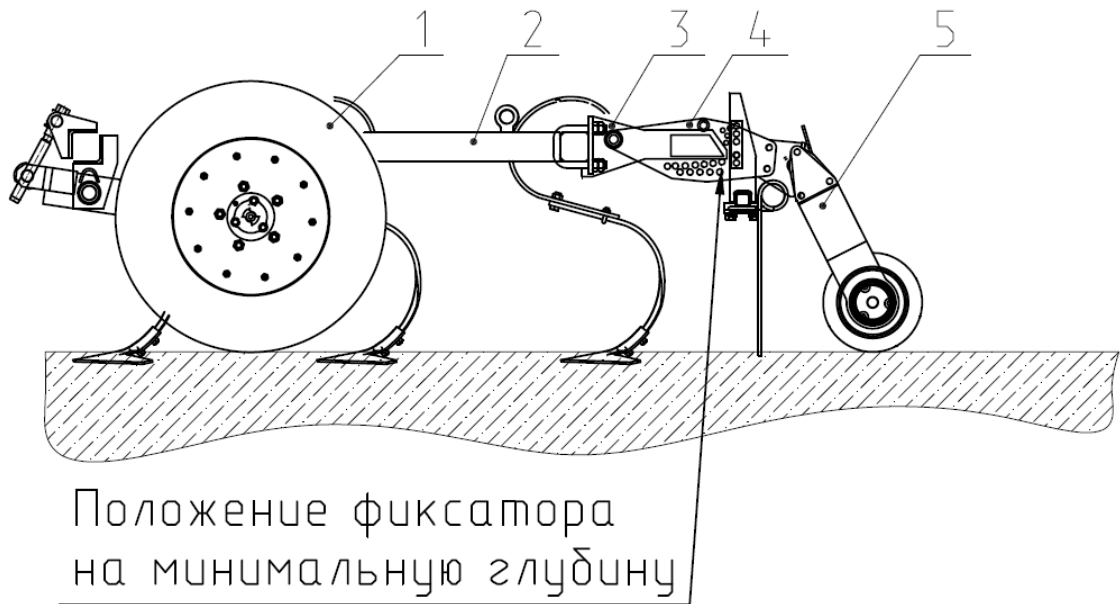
Установка глубины обработки рабочих органов катками однорядными.
